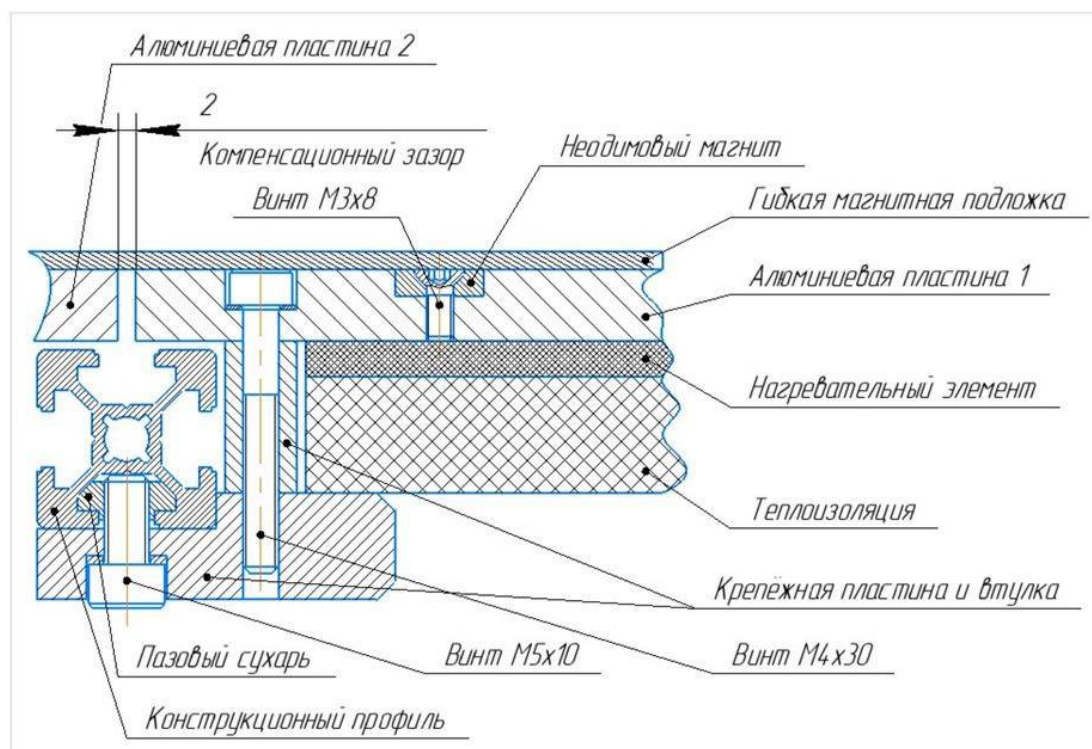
Упрощенная схема части стола в разрезе с системой крепления алюминиевых нагревательных пластин
